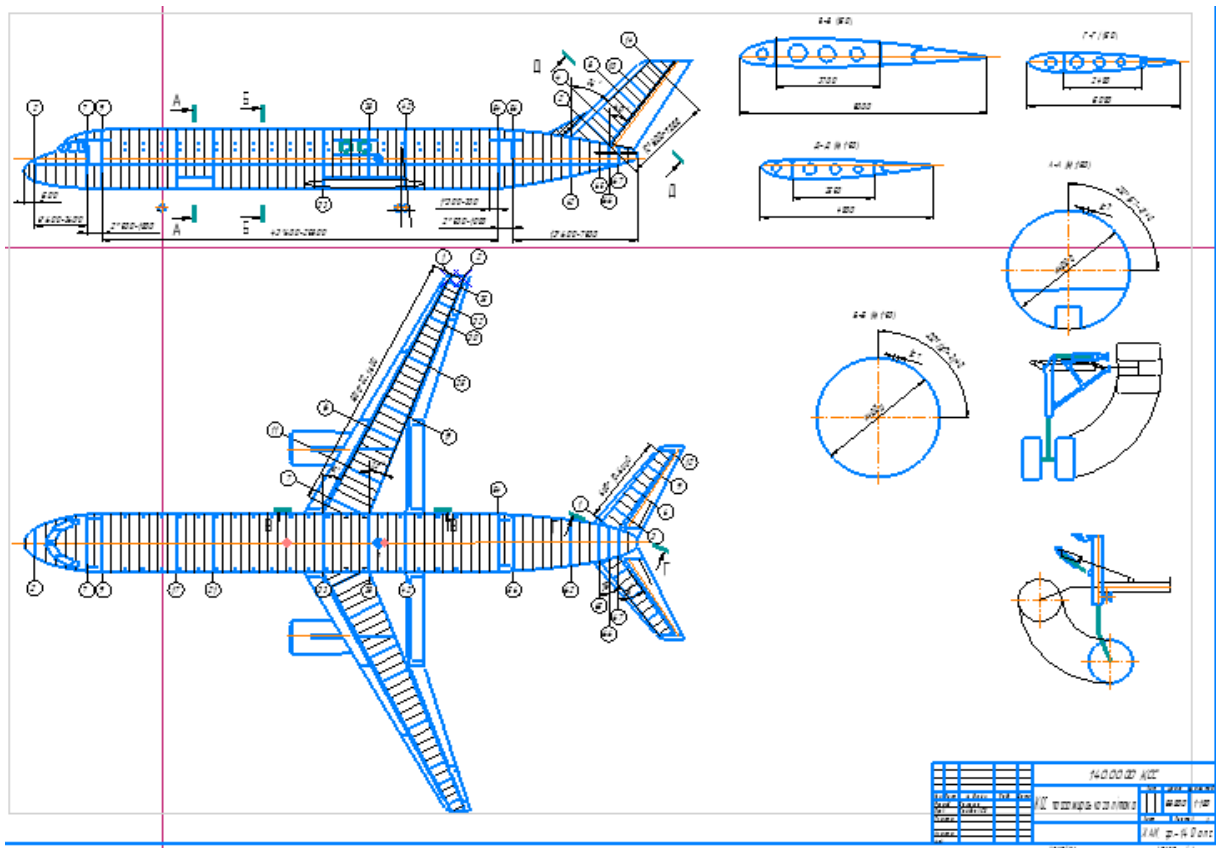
10 - Конструктивно-силова схема агрегатів літака
